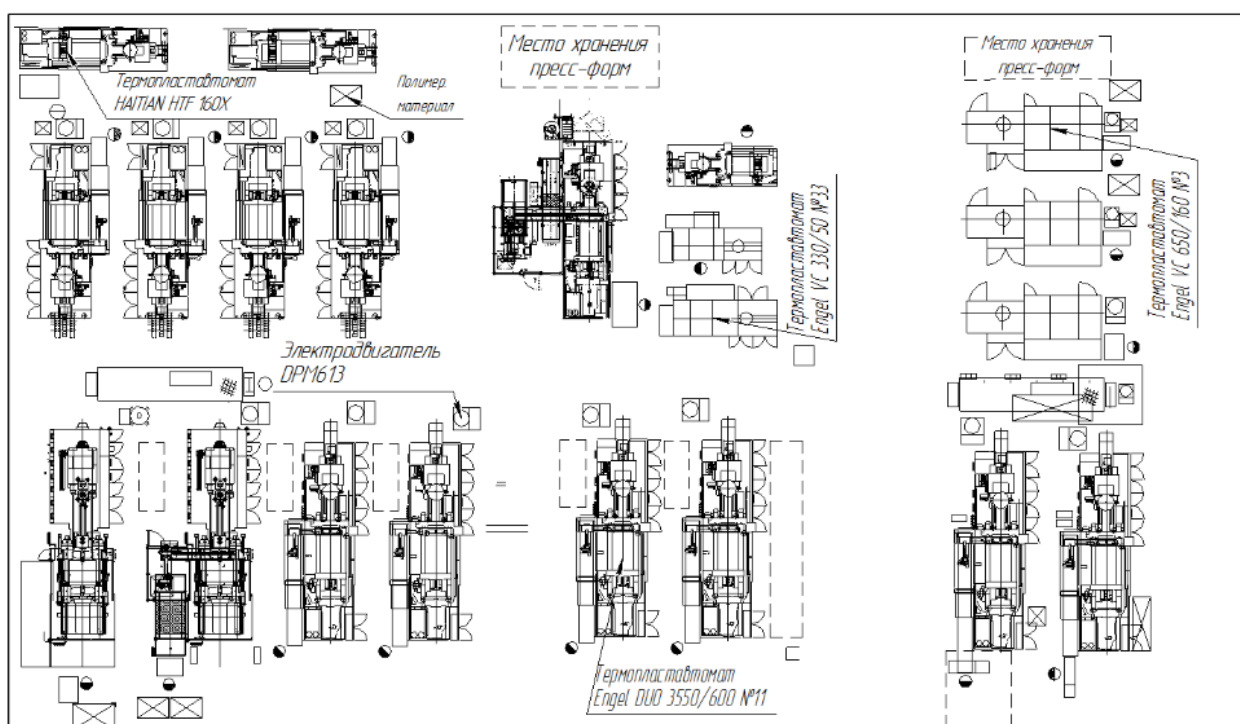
Планировка цеха литья пластмасс под давлением
